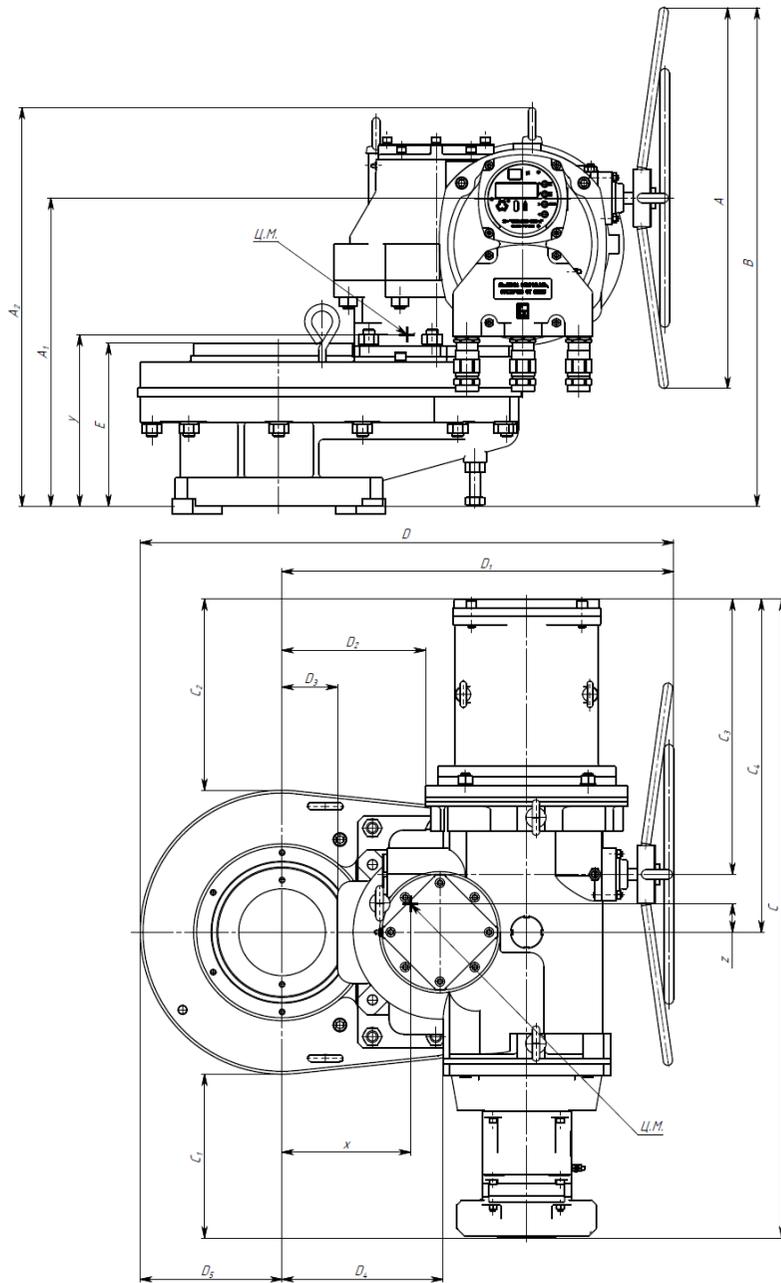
д – Габаритные размеры привода конструктивной схемы 430
